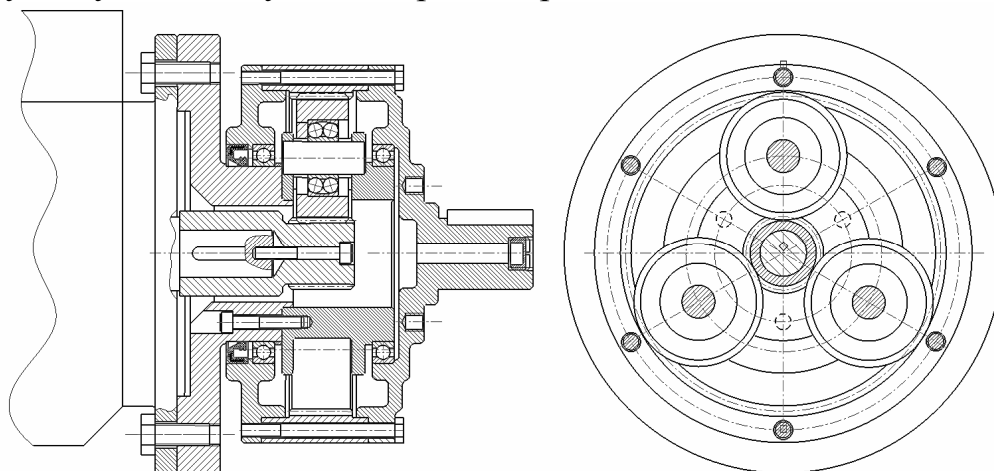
Одноступенчатый многопоточный зубчатый редуктор
